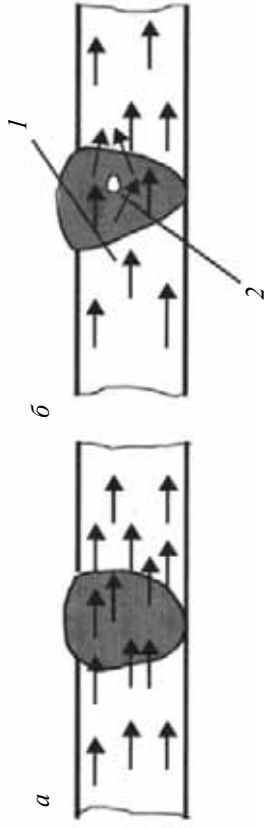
Схема прохождение магнитного потока в сварном соединении:
